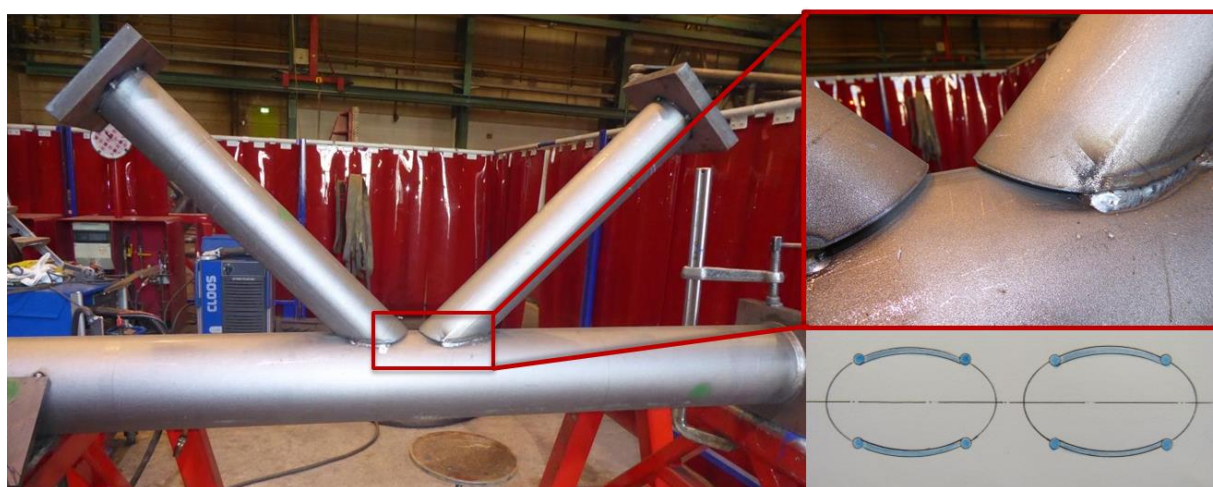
Heftschweißung bei kleinen KHP K-Knoten
